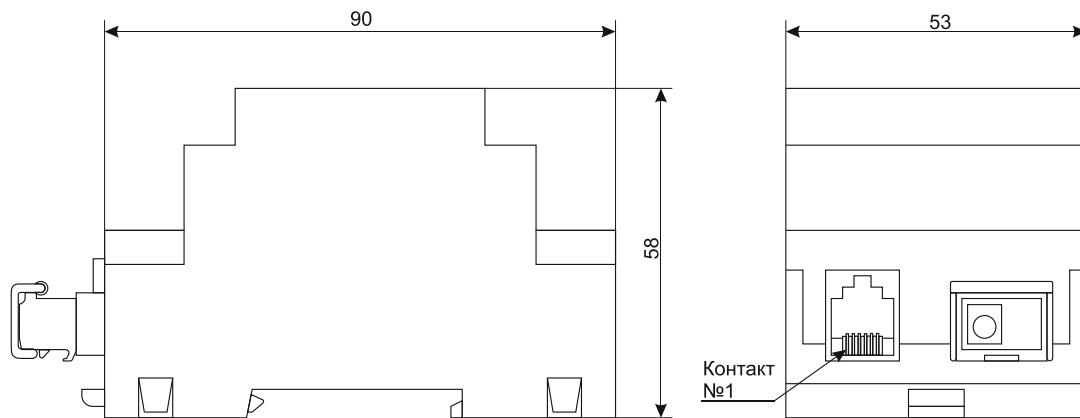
Габаритные размеры и местоположение первого контакта разъема RJ25
